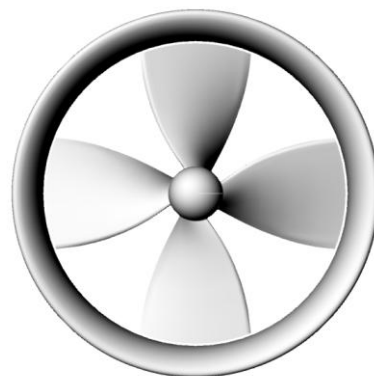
Conjunto Tubulão e Propulsor Desenhado
